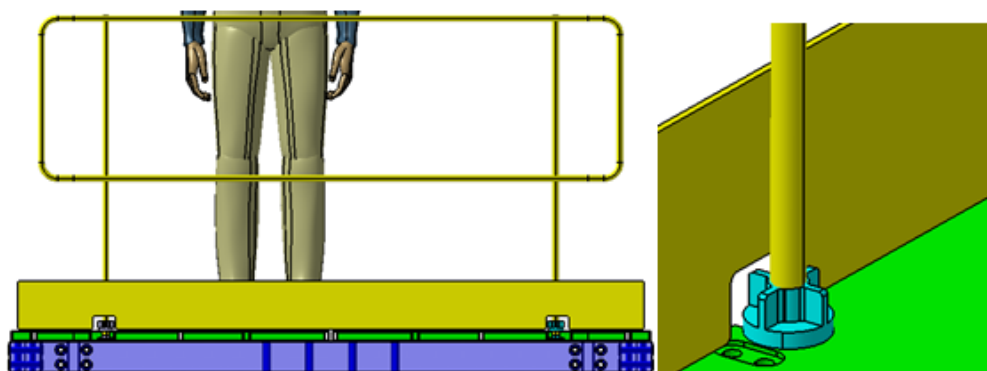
Izquierda, diseño del conjunto barandilla rodapié; derecha, detalle de soldadura del rodapié a la barra y accesorio de unión al suelo.
